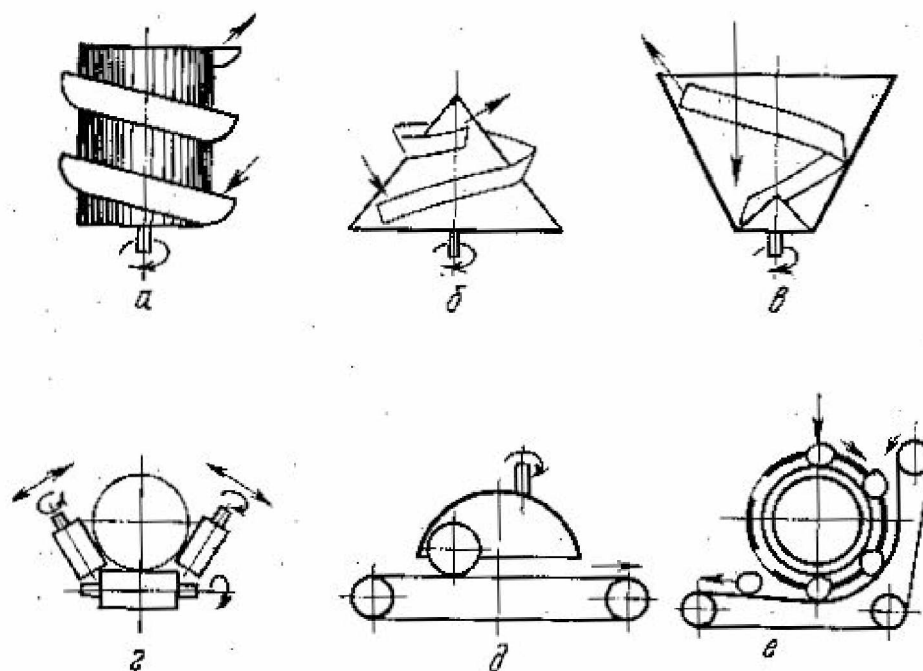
Схеми тістоокруглювальних машин: *а* - з циліндричною несучою і спіральною формувальною поверхнями; *б* - з конічними рухомою і зовнішньою спіральною формуючою поверхнями; *в* - з конічною рухомою і внутрішньою спіральною формувальною поверхнями; *г* - з горизонтальним стрічковим несучим органом і двома нахиленими стрічковими формуючими органами; *д* - з горизонтальним стрічковим несучим органом і сферичним формуючим органом; *е* - з несучим органом у вигляді барабана і формуючим у вигляді стрічкового транспортера.
